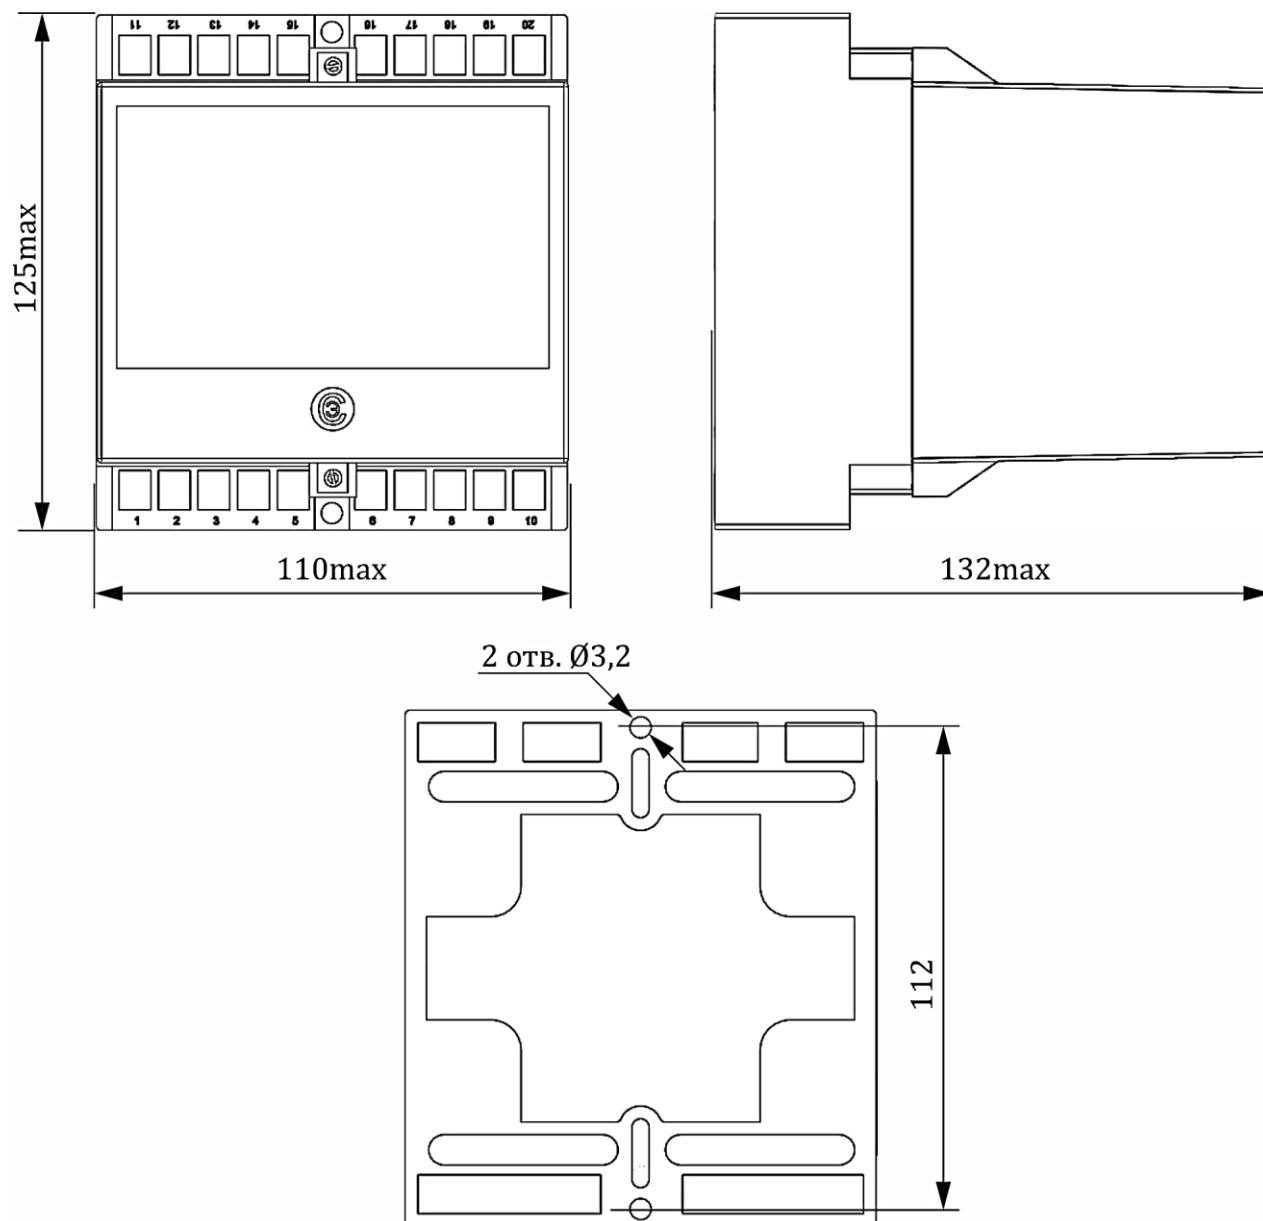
Габаритные и установочные размеры корпуса EB20
